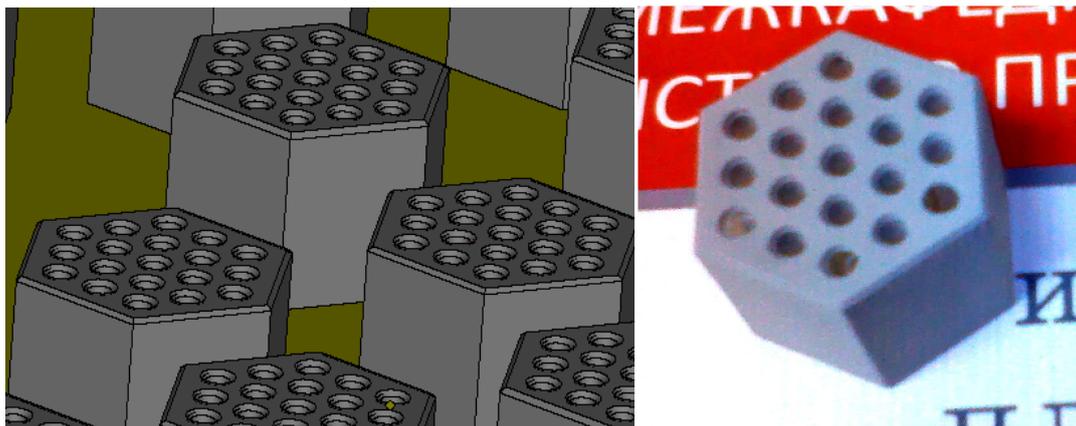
Модель сотового заполнителя для гидравлических испытаний
